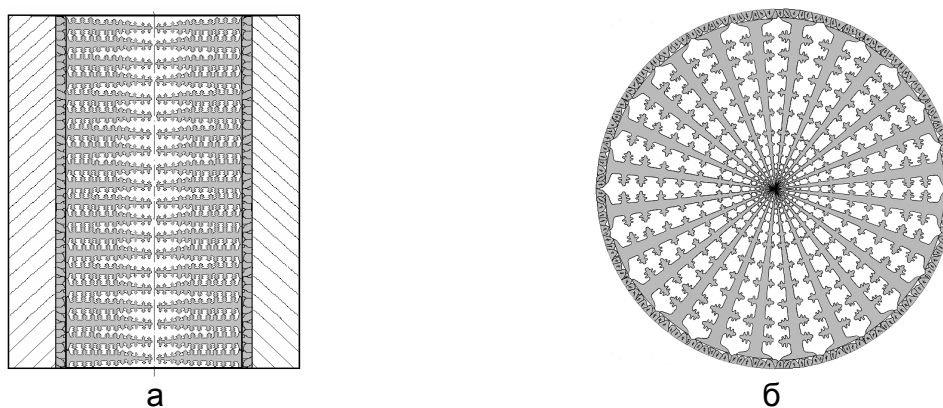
Схема гетерогенного механизма затвердевания центральных зон отливок плоской (а), цилиндрической и шаровой форм (б) с центрами кристаллизации - дендритами твердой фазы при сужении фронта затвердевания
